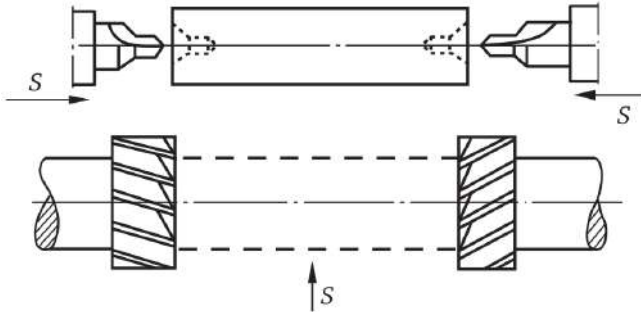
Оброблення центрових отворів на фрезерно-центрових верстатах
